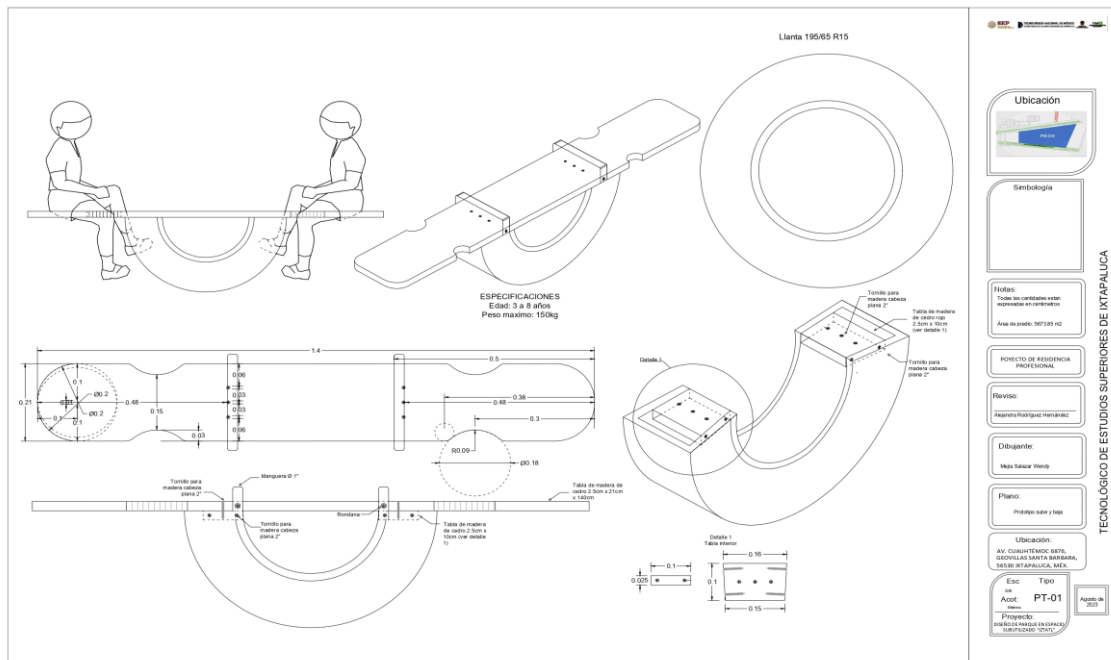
Plano de Prototipo Sube y Baja. Fuente: Elaboró Mejía, W en AutoCAD®
